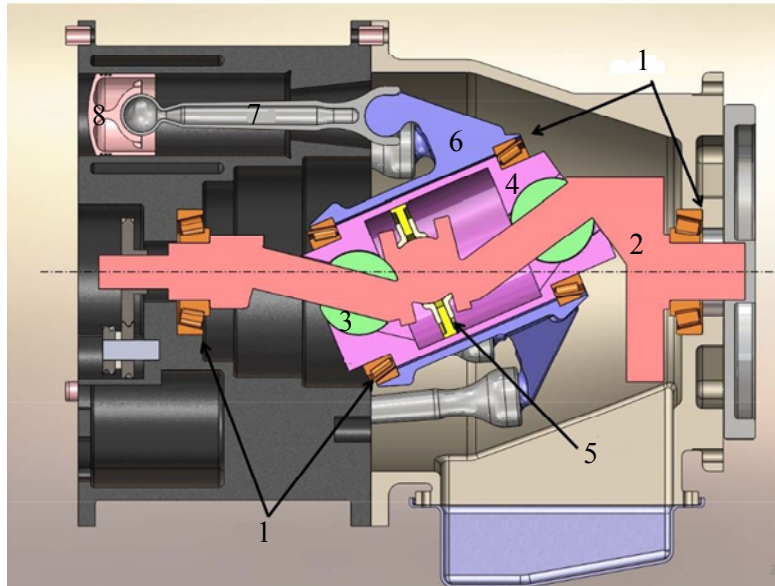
Двигун з безступінчастою зміною робочого об'єму: 1 – підшипник; 2 – колінчастий вал; 3 – втулка; 4 – муфта; 5 – активний поршень; 6 – тримаюча корона; 7 – шатун; 8 – поршень
